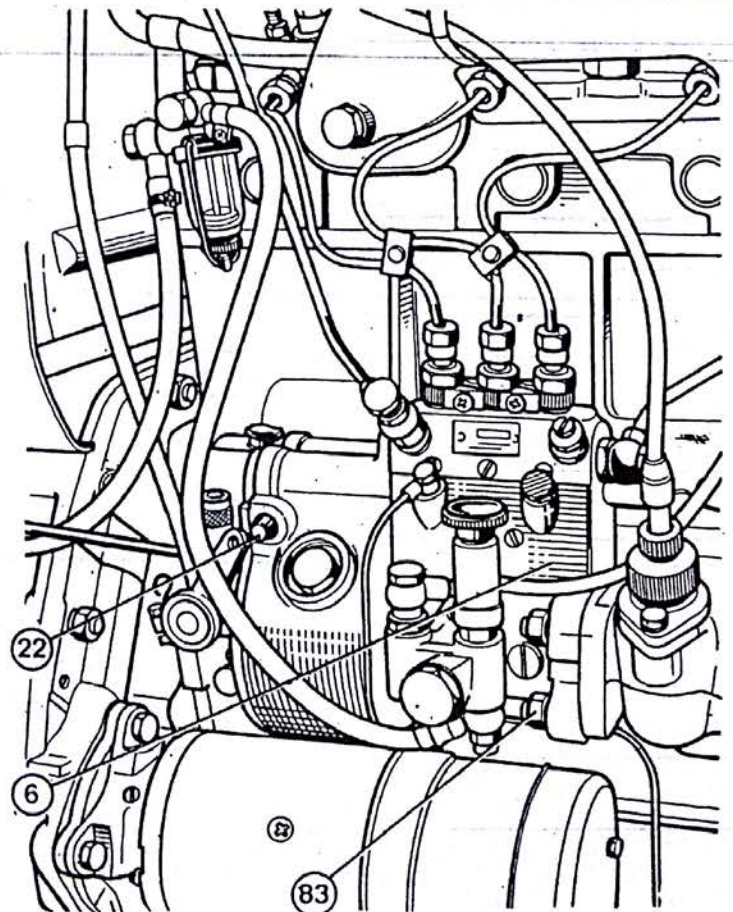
/6 - Vue de la pompe d'injection avec régulateur R.P.V.A.
